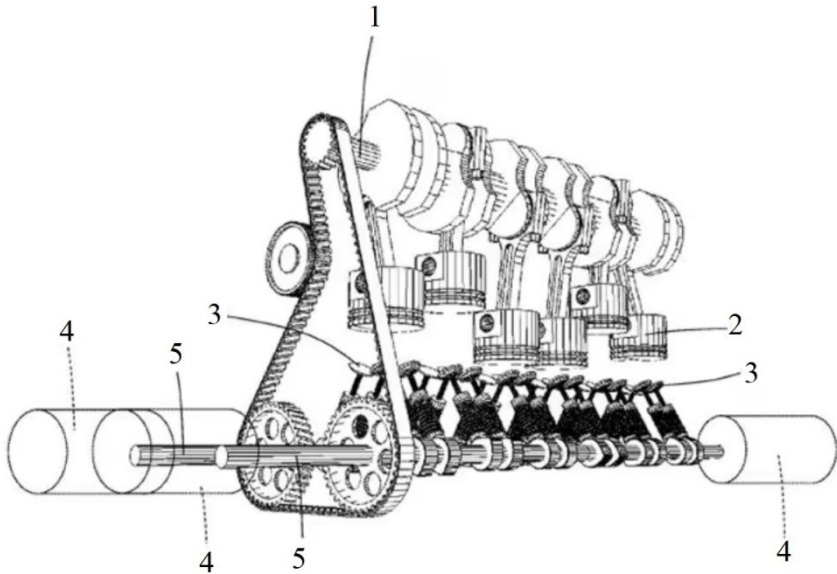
Перевернутий рядний 6-циліндровий двигун Ferrari [1]
